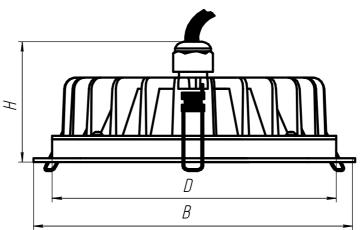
Общий вид, габаритные и присоединительные размеры светильника ДВО59.
